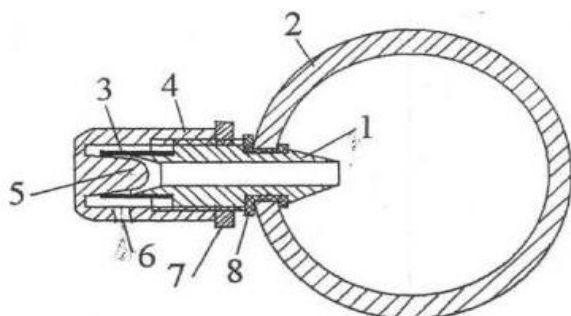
Капельница (1-штуцер; 2-поливной трубопровод; 3-резиновая трубка; 4-крышка; 5-конусообразный выступ; 6-отверстия; 7- контргайка; 8- прокладка)
